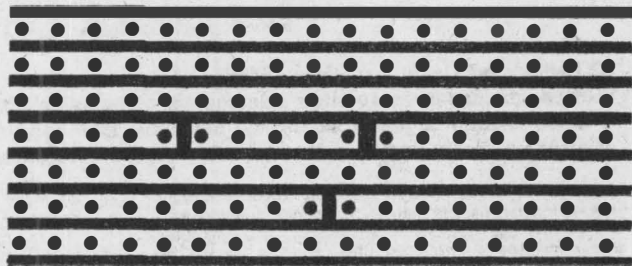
Sugestão da plaqueta de circuito impresso universal vista pela face cobreada.
